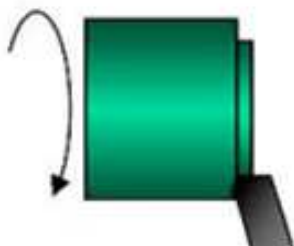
Soustružnické operace s příslušnými nástroji. [12]
